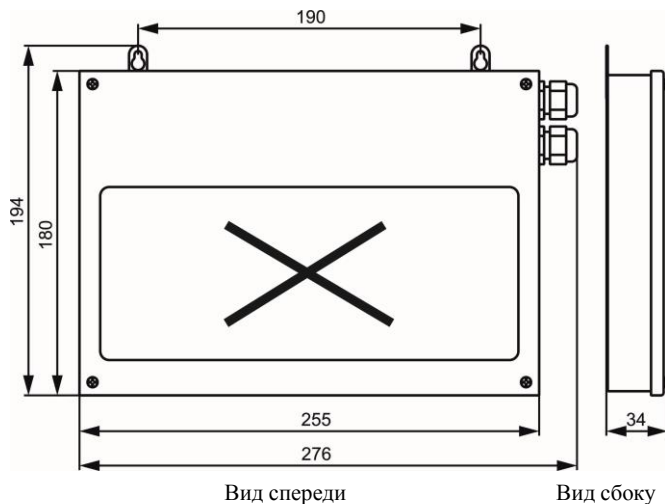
Внешний вид, габаритные и установочные размеры корпуса оповещателя
